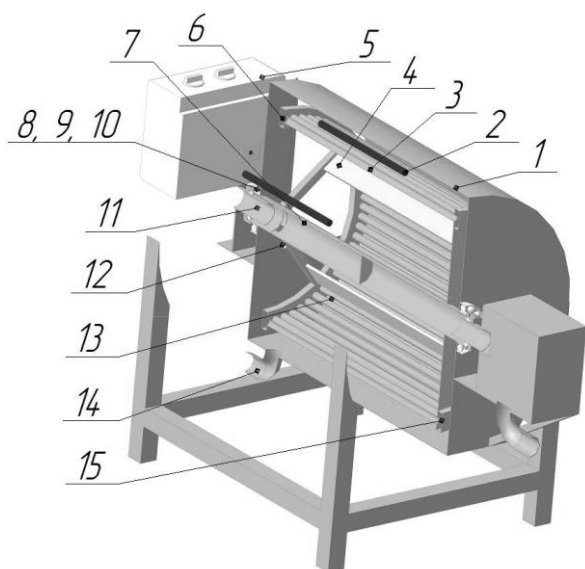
СВЧ установка для массирования и термообработки кускового мясного сырья: 1 – цилиндрический экранирующий корпус; 2 – ИК лампы; 3 – трубчатая резонаторная камера; 4 – лопасти; 5 – генераторный блок с магнетроном и излучателем; 6 – кольцевая труба; 7 – полый вал; 8 – подшипниковый узел; 9 – диэлектрическая прокладка; 10 – стопорная гайка; 11 – муфта; 12 – люк; 13 – щель между трубами; 14 – сливной патрубок, 15 – полый диск
